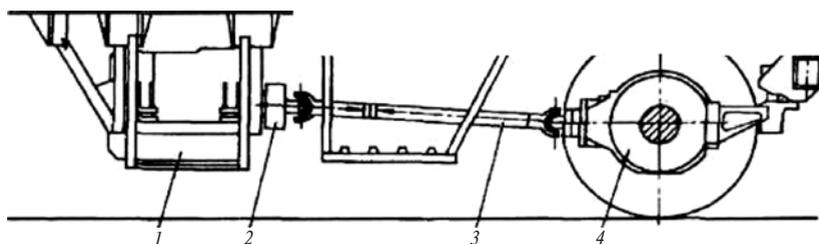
Редукторно-карданный привод генератора от средней части оси колесной пары: 1 – генератор; 2 – упругая резиновая муфта; 3 – карданный вал; 4 – редуктор
